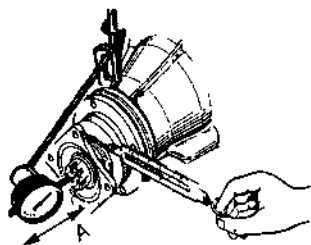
Проверка затяжки подшипника ведущего зубчатого колеса и осевого зазора
